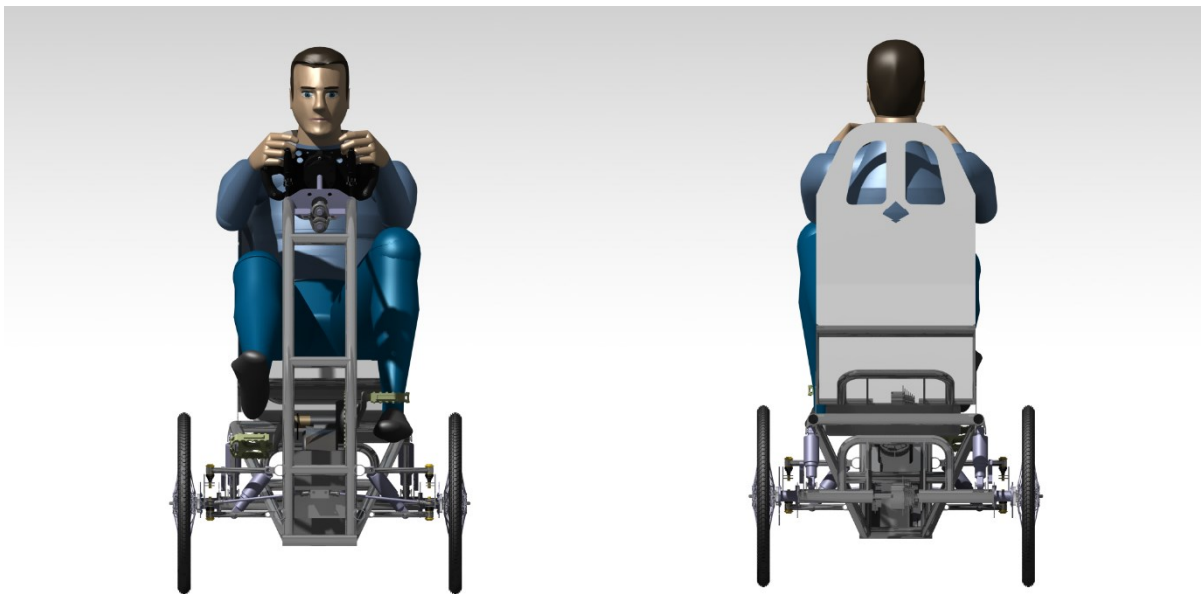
Vista frontal e posterior da estrutura do E-Pedal. Fonte: Elaborado pelo autor.
